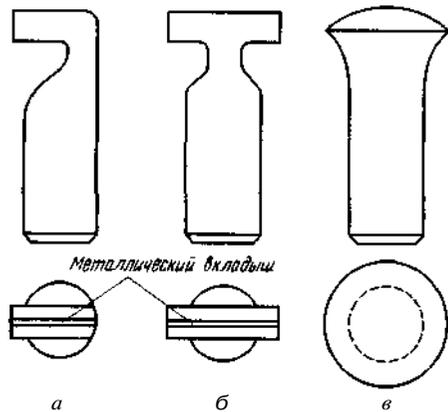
Китштоки (сверху — вид спереди, под ним — вид сверху): а — односторонний для колец, б — двусторонний для колец, в — плоский для всех остальных видов изделий
